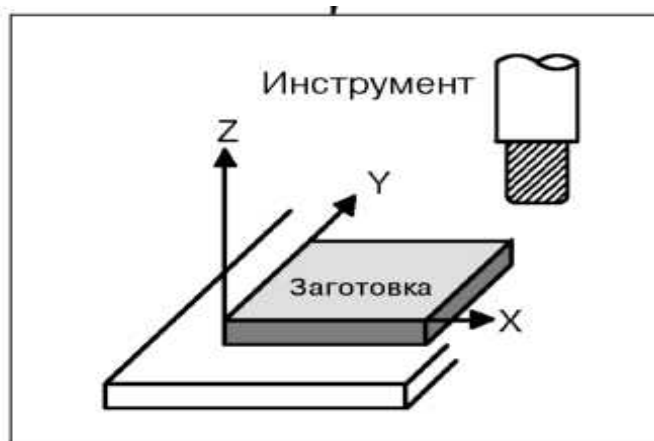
Система координат рабочего пространства трехкоординатного станка с вертикальным расположением шпинделя
